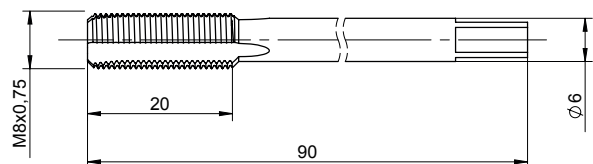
Gewindebohrer M8x0,75 tap Typ 1361
